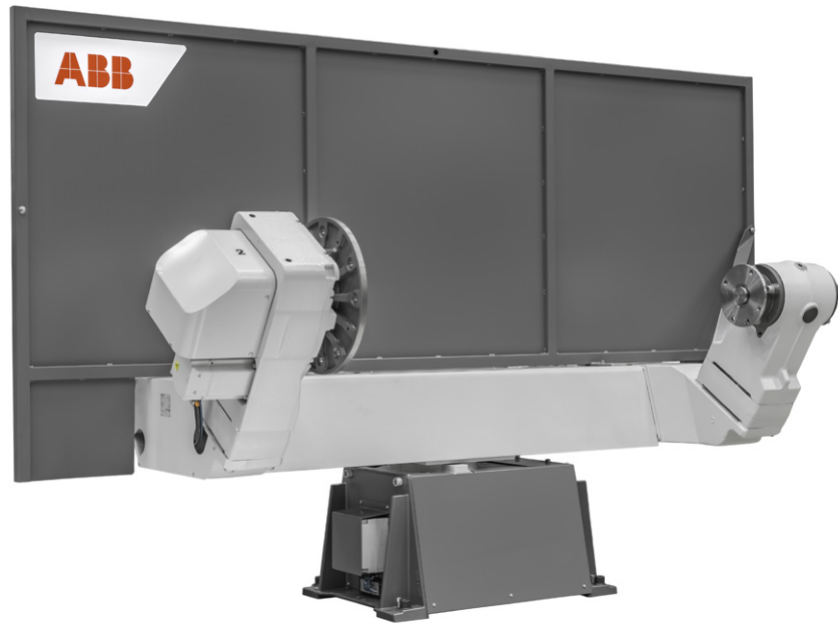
Posicionador* ABB IRBP R-1000/1000 empleado en este proyecto. El objetivo del posicionador es alternar la posición del útil entre zona de carga por parte del operario y zona de soldadura por parte de los robots. Además, en este caso, lleva incorporado un *motorreductor* que añade un *eje de giro externo* al utillaje, lo que añade a este 1 *gdl* y permite a las antorchas de soldadura acceder a los cordones más complicados. Fuente: ABB (2018).
